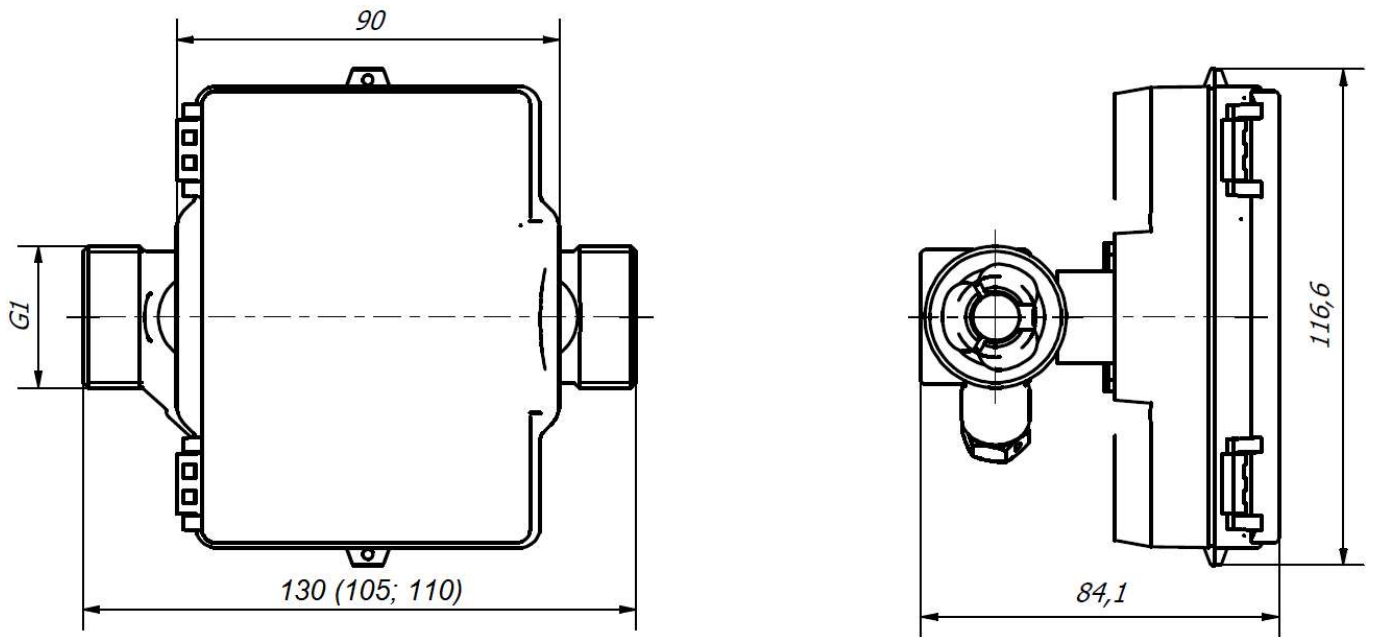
Gjengede endetilkoblinger G1", monteringslengde L=130 mm (eller L=105 mm eller L110 mm).
